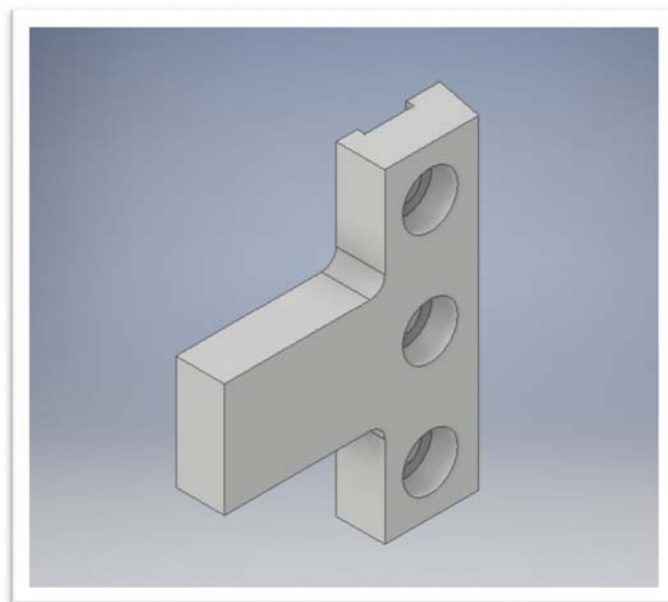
Detalle pieza a soldar (Fotogrametría)
